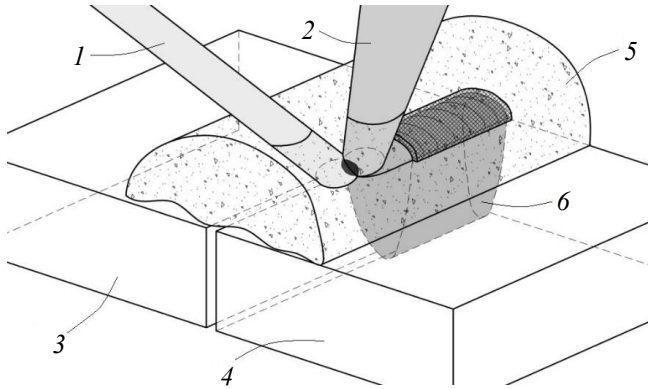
Условная схема процесса лазерной сварки по слою флюса
